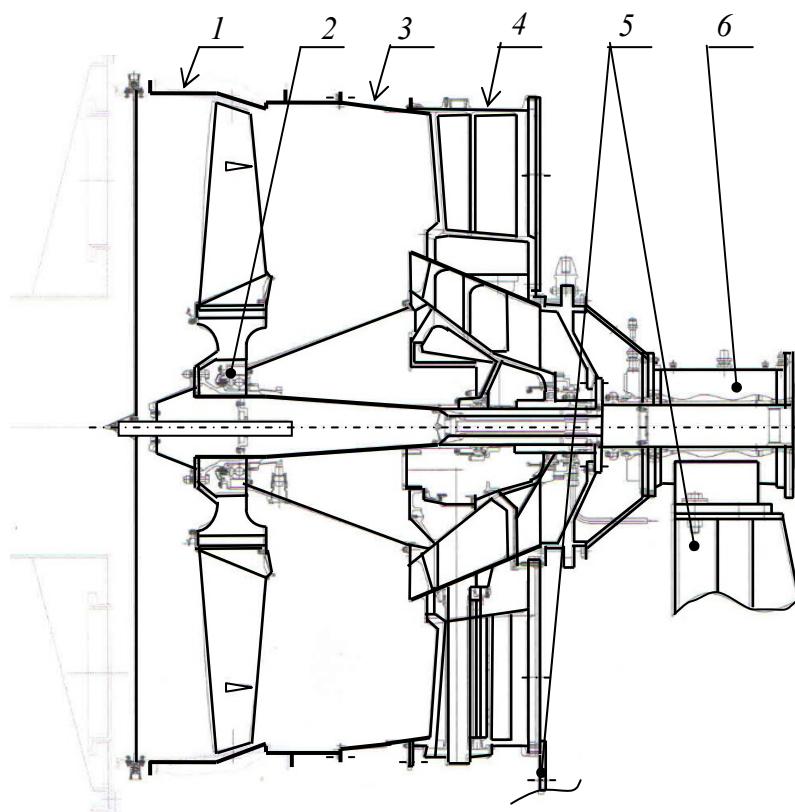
Схема установки для испытаний корпуса вентилятора: 1 – корпус вентилятора; 2 – рабочее колесо вентилятора; 3 – корпус спрямляющего аппарата; 4 – разделительный корпус; 5 – элементы рамы установки; 6 – электропривод
